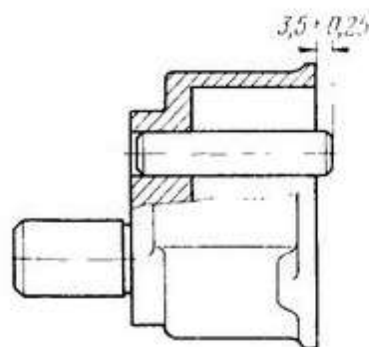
Корпус масляного насоса с осью ведомой шестерни в сборе
